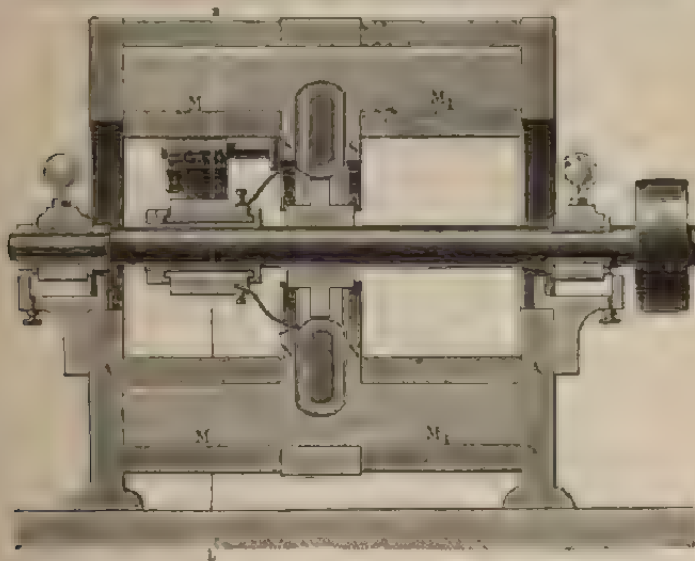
Flachringmaschine von Schuckert. (Längenschnitt.)
